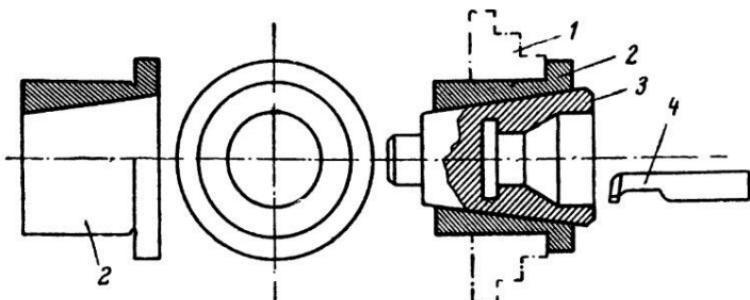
Конусная втулка-оправка и ее применение: 1 — кулачки патрона; 2 — втулка; 3 — обрабатываемая деталь; 4 — резец.
